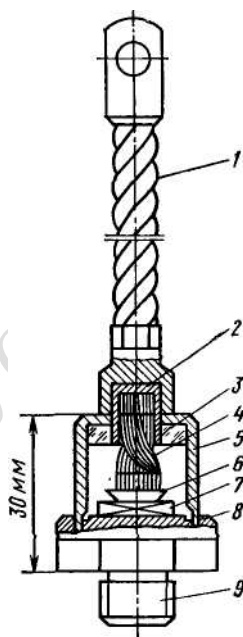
Конструкция мощного кремниевого диода ВЛ-200: 1 — внешний гибкий вывод (анод); 2 — стакан; 3 — стеклянный изолятор; 4 — внутренний гибкий вывод анода; 5 — корпус;
